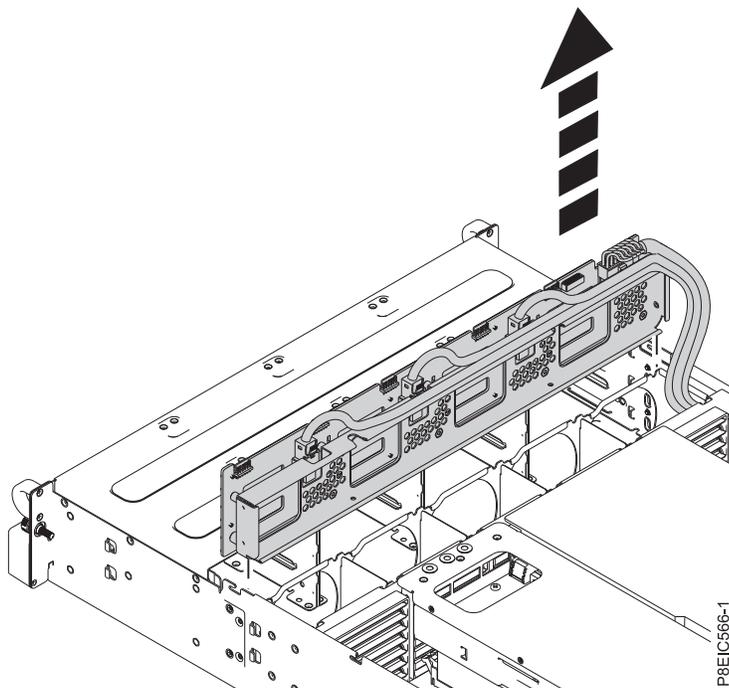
Rückwandplatine des Laufwerks ausbauen
